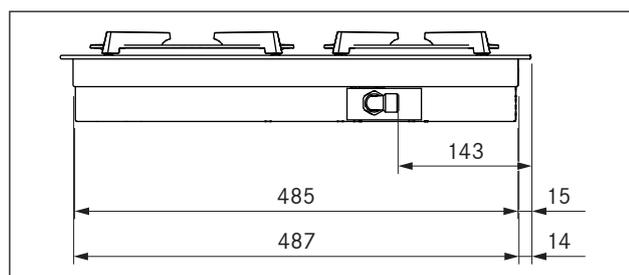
Dimensioni apparecchio CKG vista laterale
